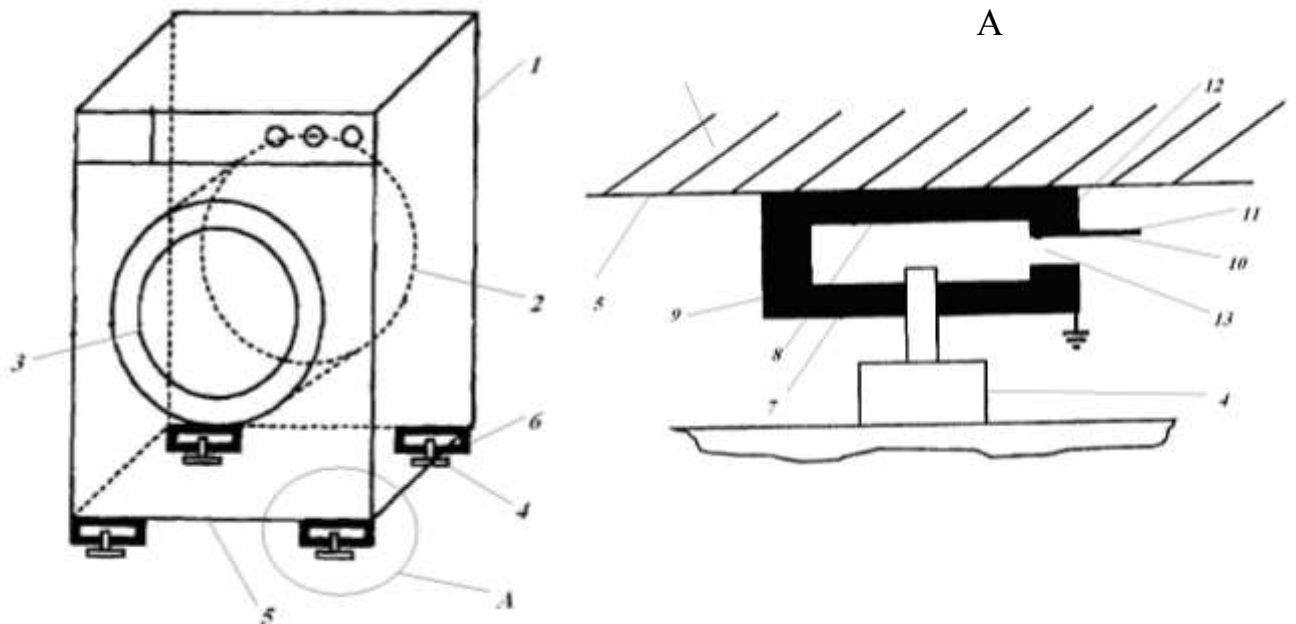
Пристрій для обробки білизни із пристроєм вимірювання ваги
